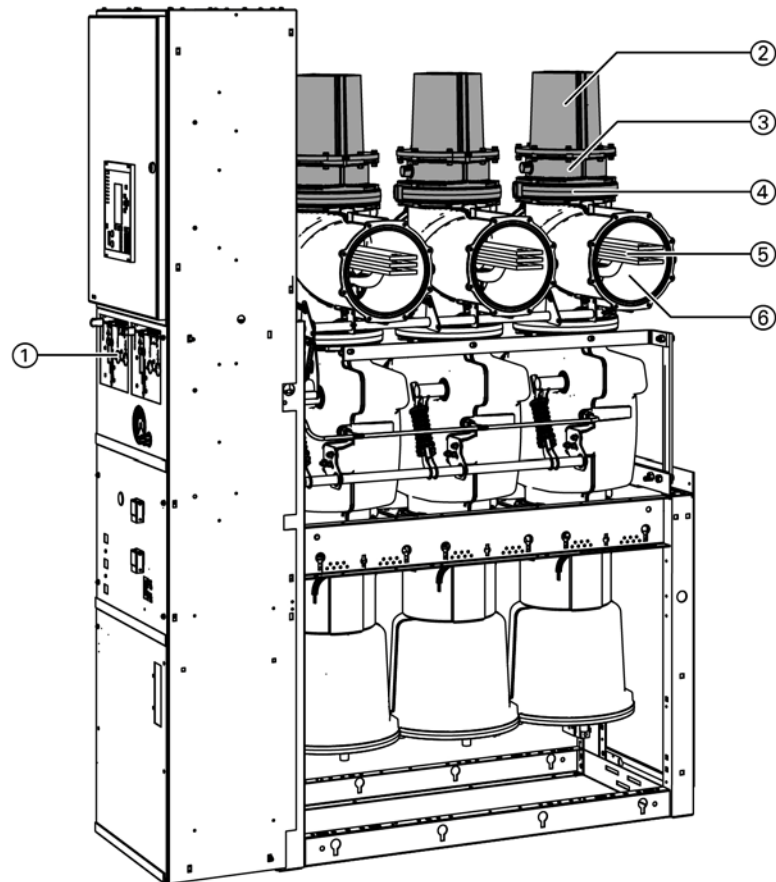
Обзор компоновки сборных шин: подключение сборных шин с помощью штекера размера S2 или S3 с трехпозиционным разъединителем
